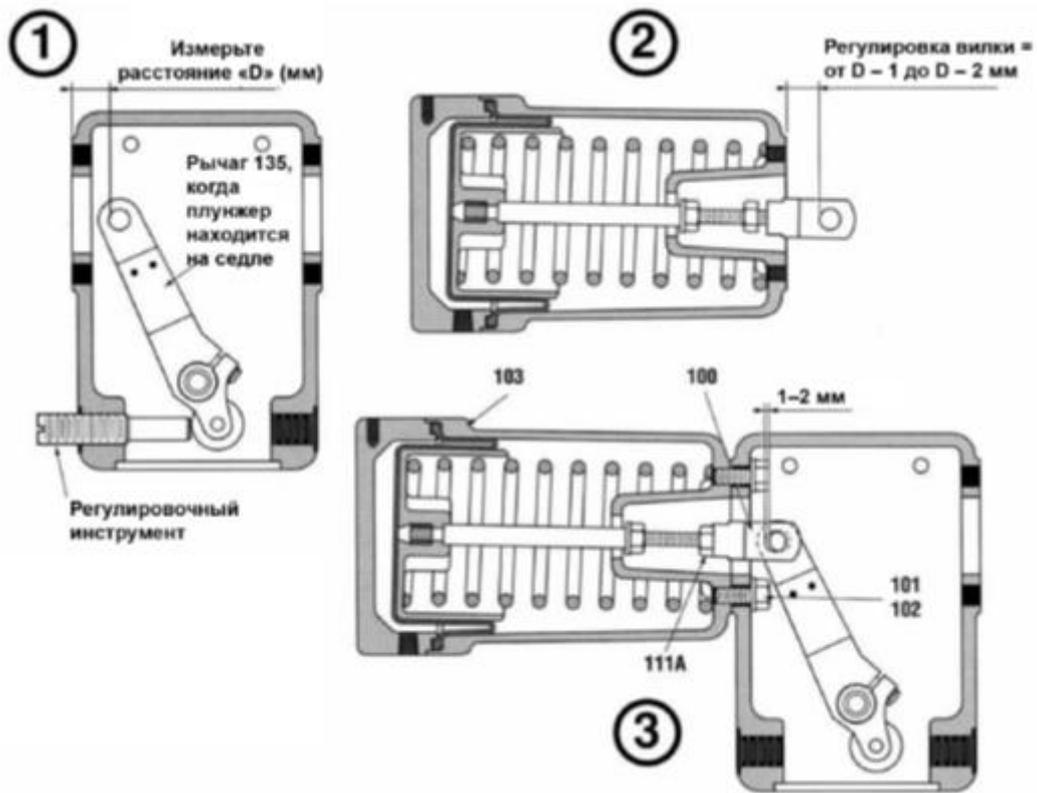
Регулировка привода для нормального закрытого положения (при прекращении подачи воздуха клапан закрывается)
